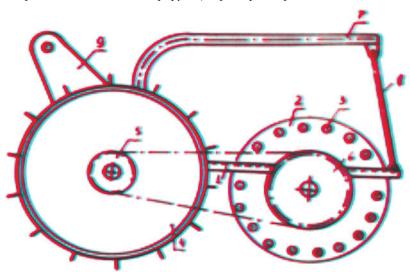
Навеской каток-сепаратор Котельникова В.Я.: 1 – рама; 2, 3 – сепарирующий ротор; 4 – тормозное колесо; 5, 6 – цепной привод от колеса на ротор; 7, 8 – подвесной кронитейн; 9 – навесное устройство
